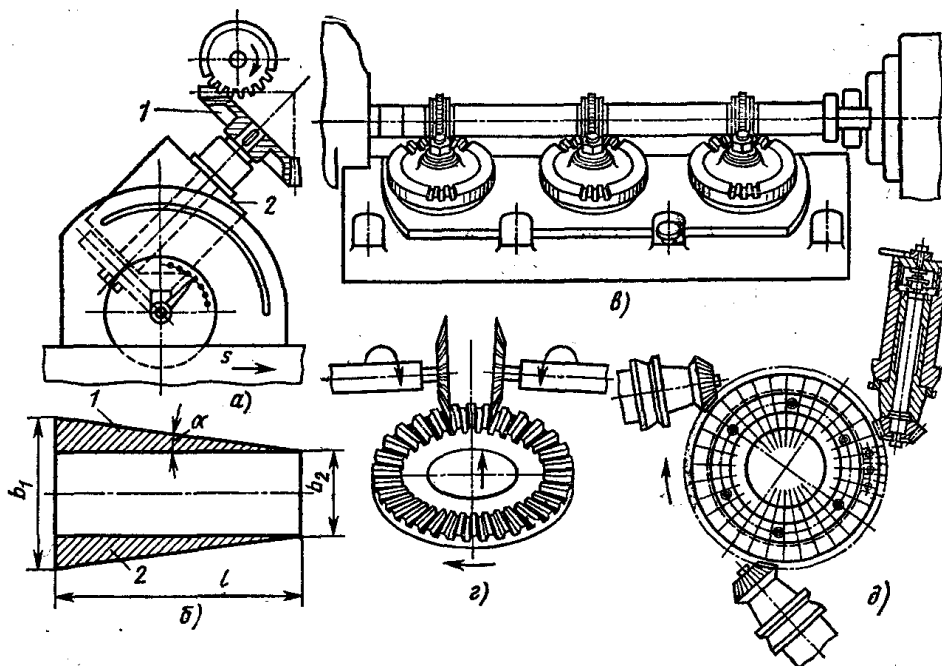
Схеми зубофрезерування конічних коліс
